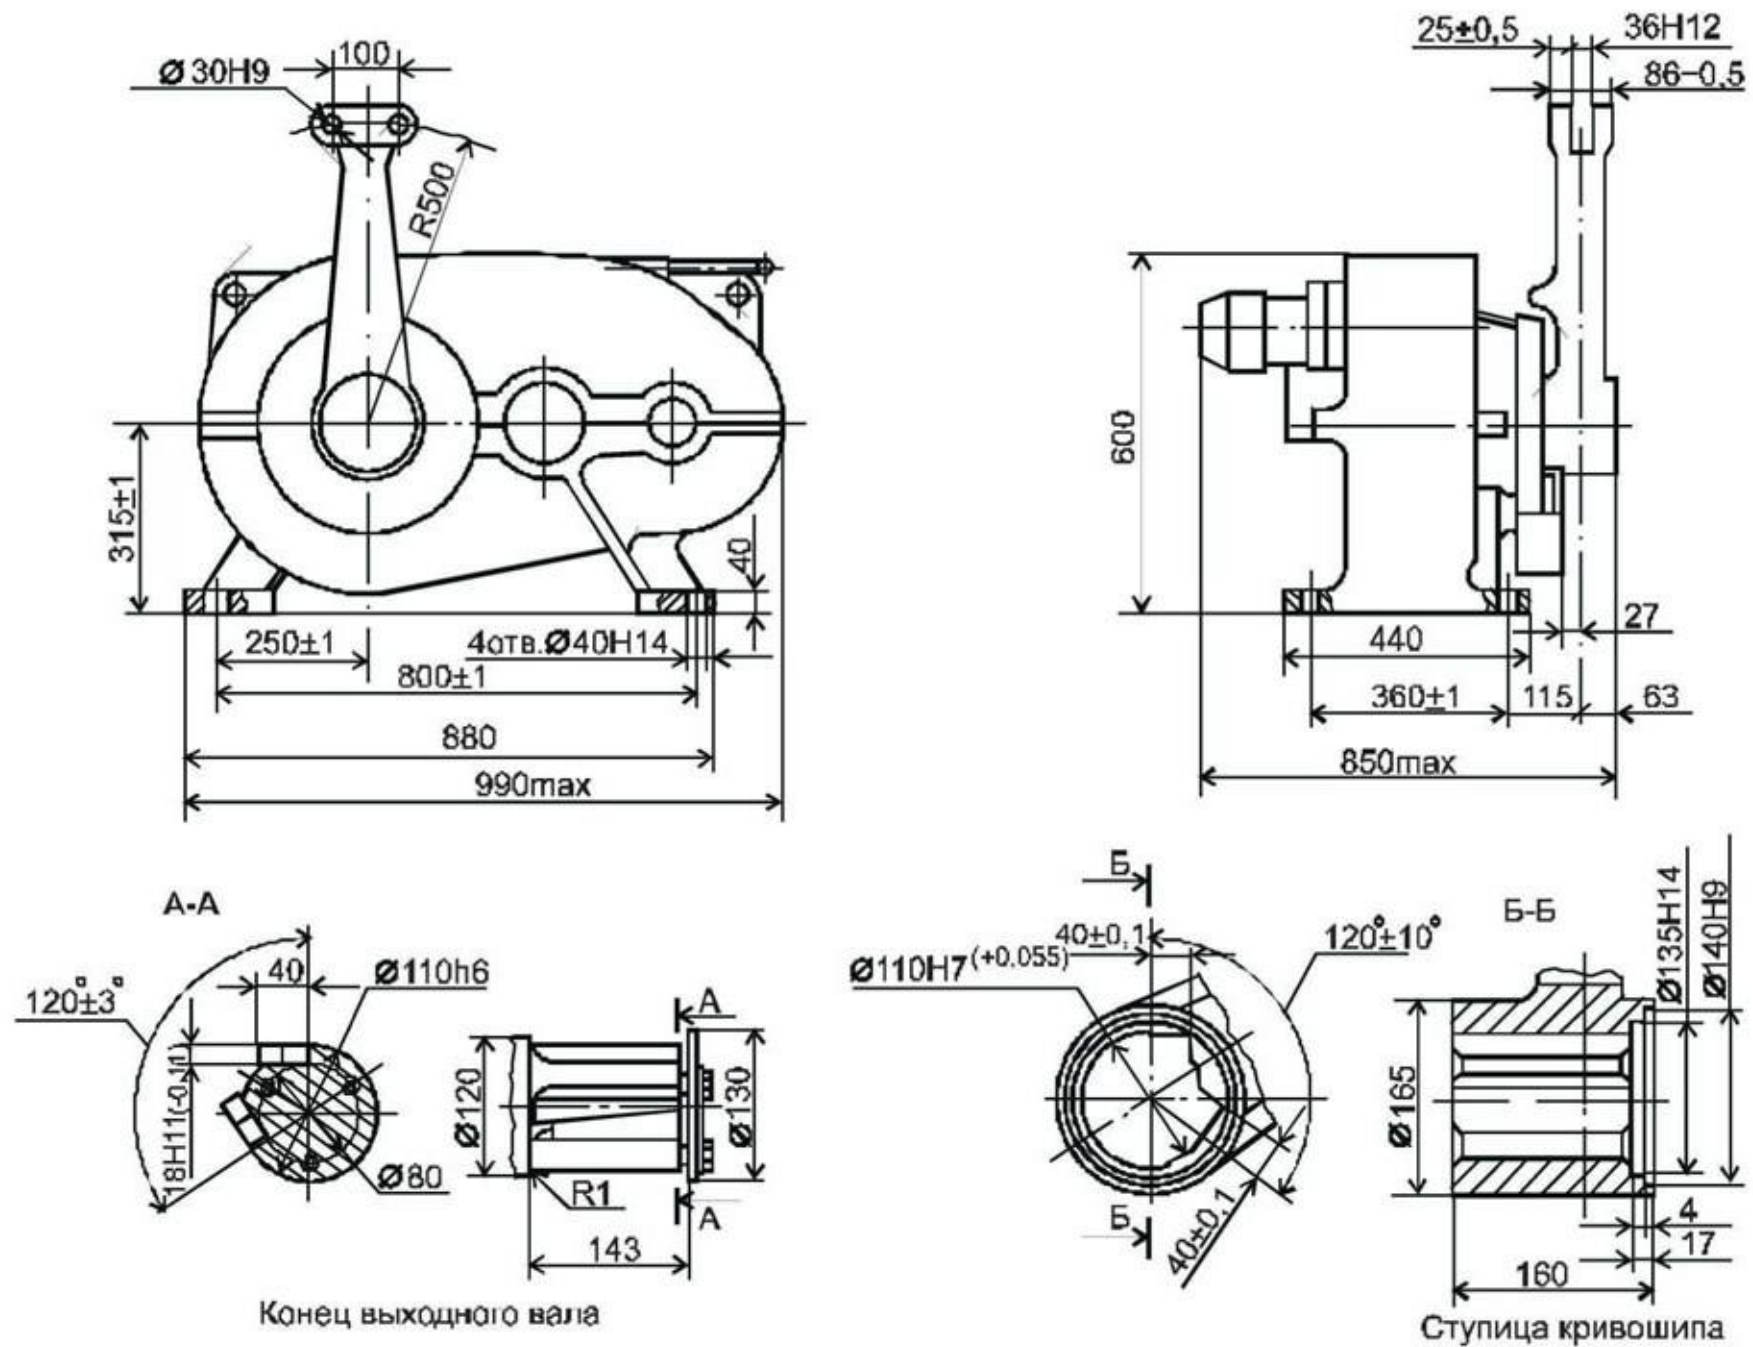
Габаритные размеры механизмов МЭО-10000-97К, МЭО-10000-97КА
